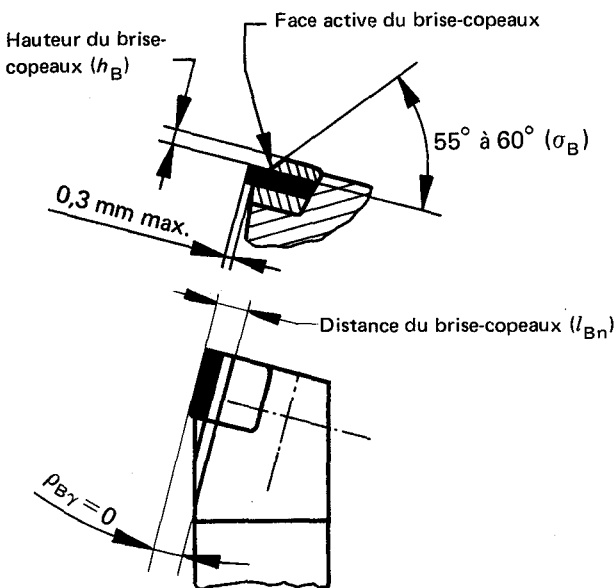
Brise-copeaux et dépassement de la plaquette
